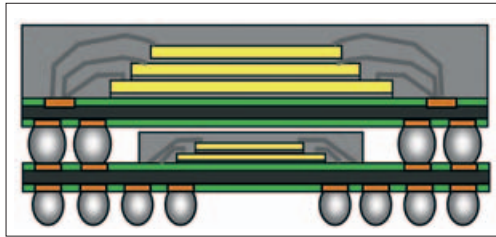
Die Package-on-Package-Technik kommt auch bei Industriebaugruppen zum Einsatz. Dabei werden zwei oder mehr BGA-Chip-Gehäuse platzsparend übereinander angeordnet. (Bild: Samsung)
